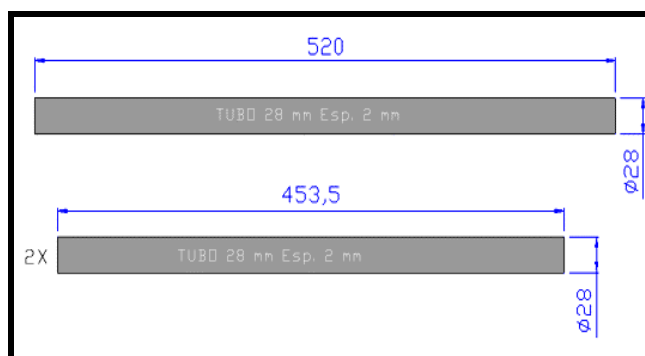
(a) – Esquema de corte do tubo de 28 mm.
